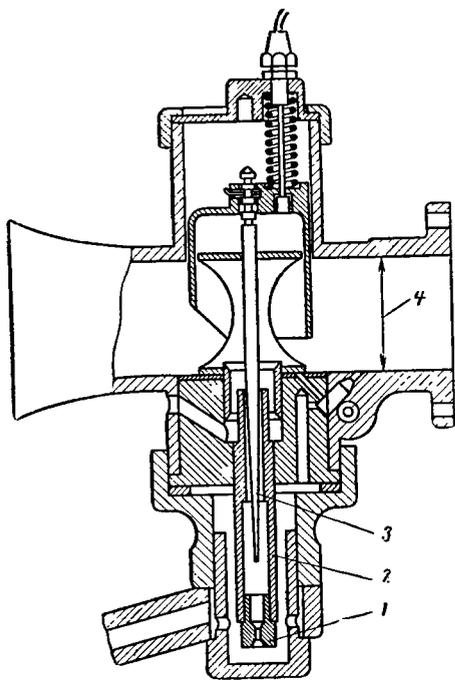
Разрез карбюратора; 1—главный жиклер; 2—распылитель; 3—игла распылителя; 4—номинальный размер смесительной камеры карбюратора.
